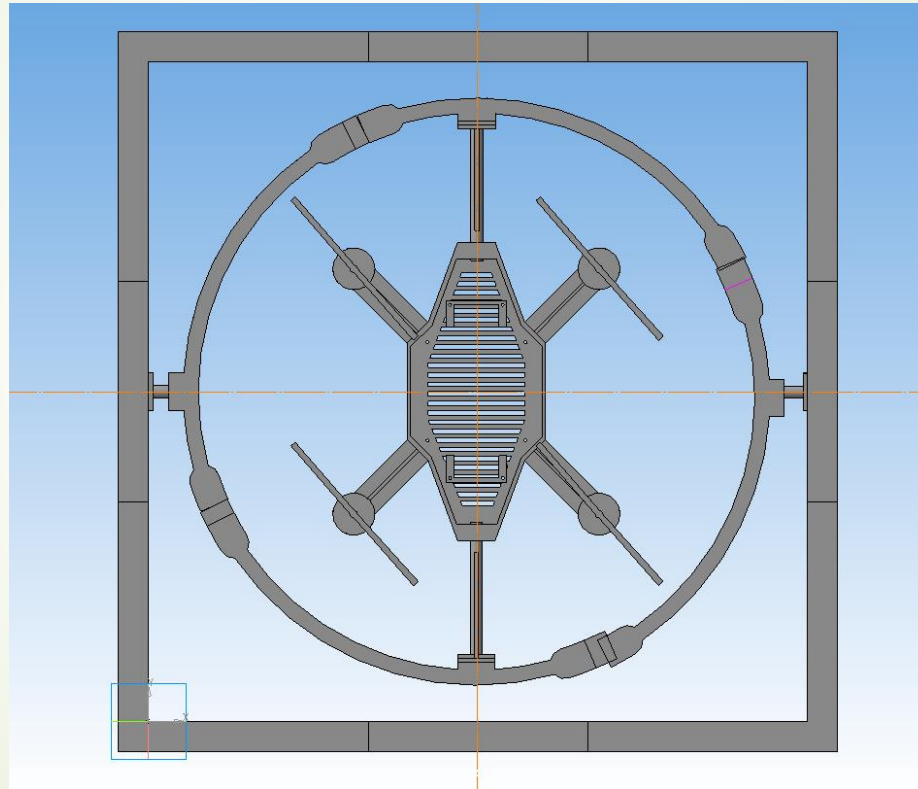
Сборка стенда САПР Компас-3D, вид сверху
